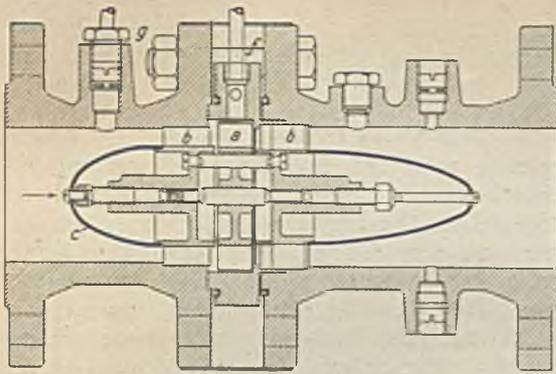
Längsschnitt durch das Zwischenstück mit der Turbine des Druckluftmessers Pionier.
